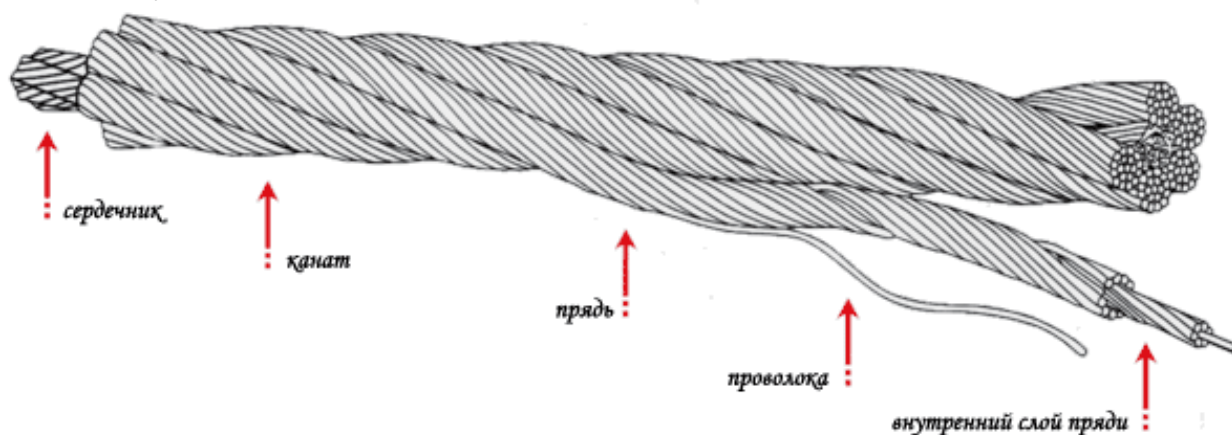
Общая конструкция стальных канатов двойной свивки
